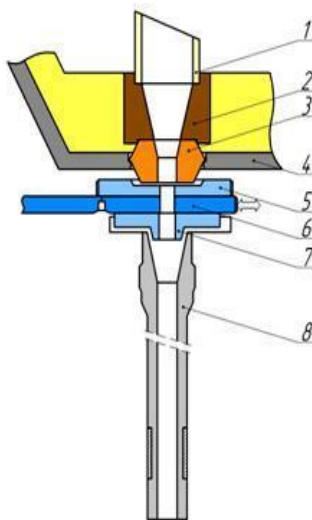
Схема подачі сталі із промковшу через триплитний шиберний затвор: 1 – стартова труба; 2 – гніздовий блок; 3 – стакан-дозатор; 4 – кожух промковша; 5 – верхня плита шиберного затвора; 6 – середня плита шиберного затвора; 7 – нижня плита шиберного затвора; 8 – занурювальний стакан.
